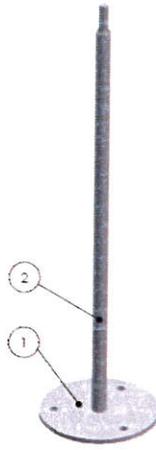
Anschlagseinrichtung, Typ: ESA Easy 300-800 III B / B-S
